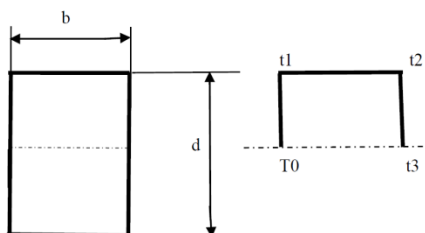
Цилиндрический вал с нанесением размеров и его кодировочная схема
